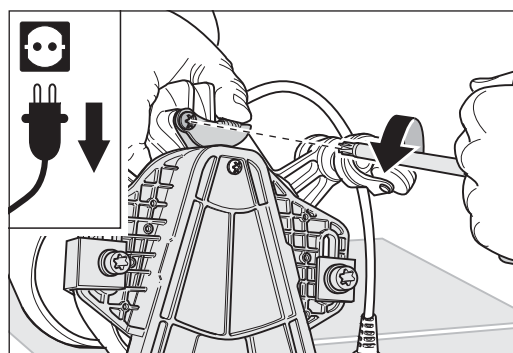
Die Schraube lösen, mit der das Riemenspannblech befestigt ist.
